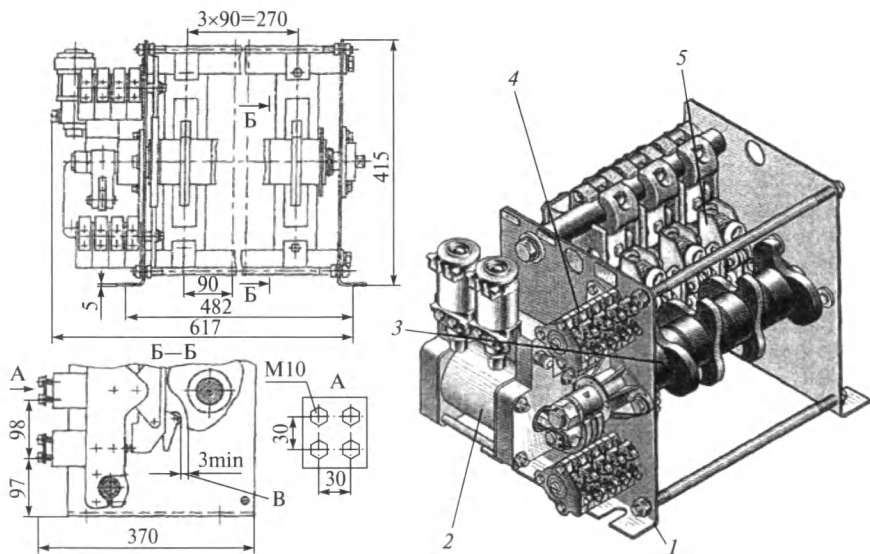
Переключатель кулачковый двухпозиционный ПКД-01
